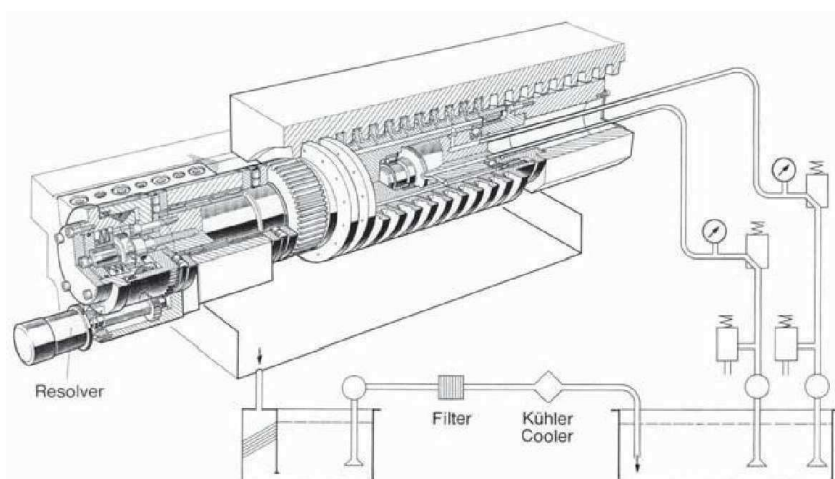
Hřeben a pastorek od firmy Stober [7]
